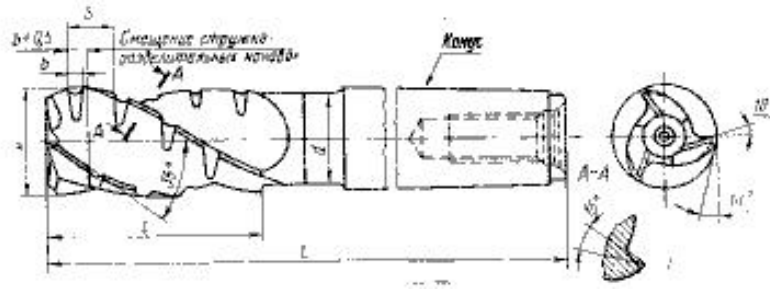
Фреза 2220-0145 P6M5 [ДСТУ17025-71]
